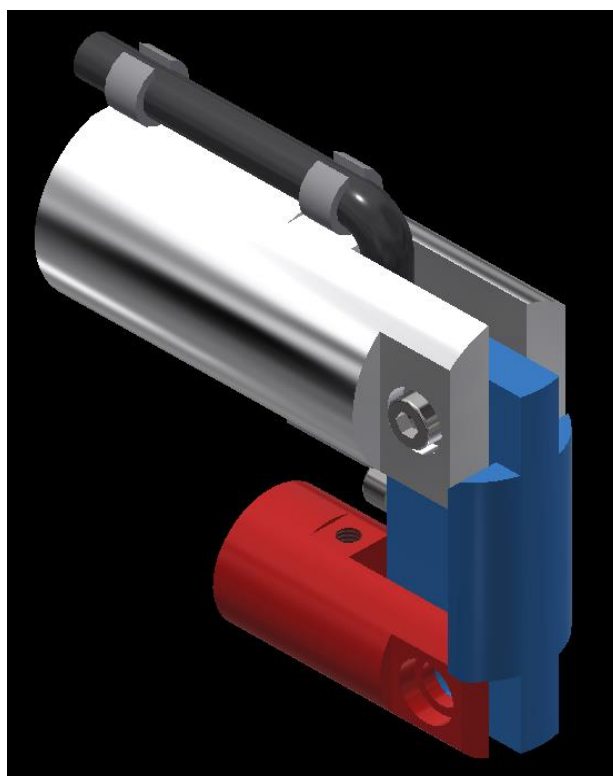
Primeiro design em CAD - Vista frontal em dobra
